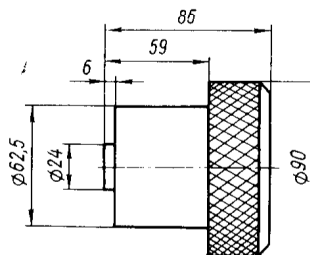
Оправка для запрессовки приводного вала в средний подшипник и зубчатого хвостовика с подшипником в сборе в кожух
